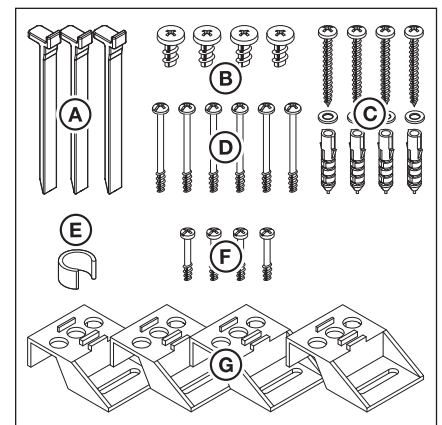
Пакет со вспомогательными принадлежностями для корпуса блока управления
